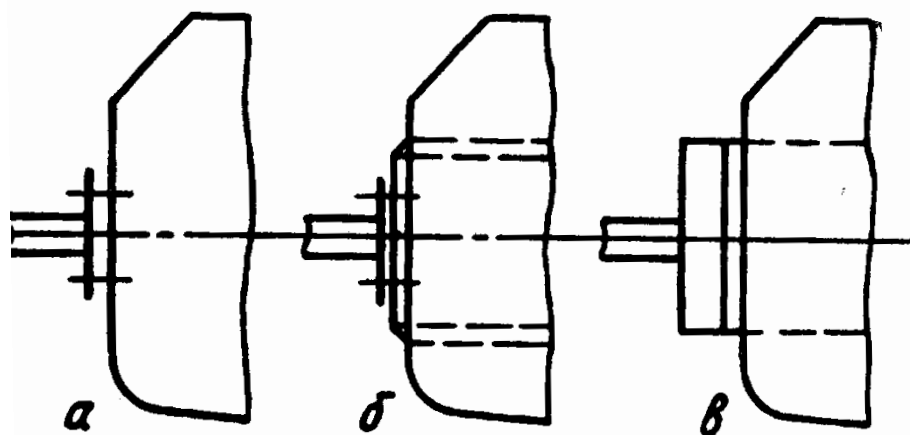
Схемы крепления цапф к корпусу (а), к усиленному корпусу (б) и к опорному кольцу (в)
